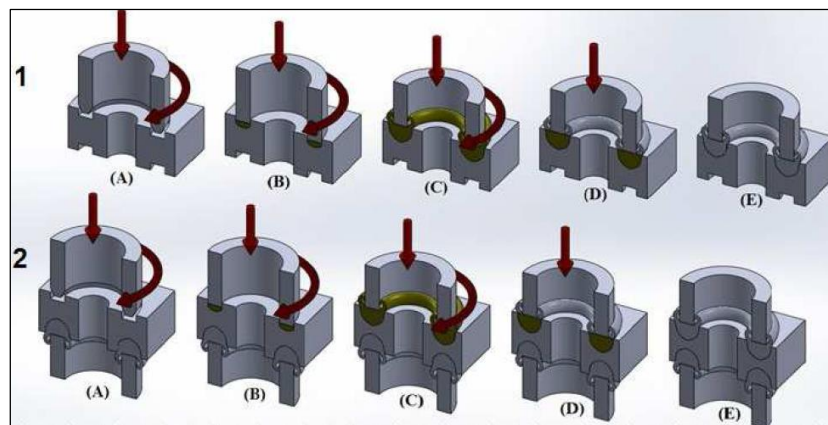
Representação do posicionamento e fixação dos tubos e anel intermediário para soldagem FW.
